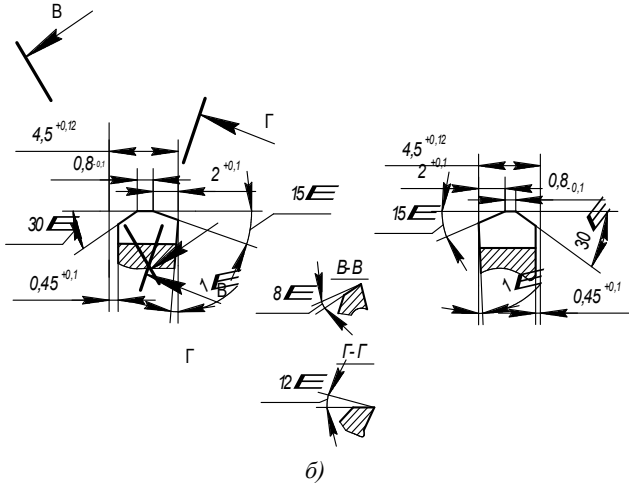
Диска фреза з клесрізьбовим з'єднанням різальної частини і хвостовика:
